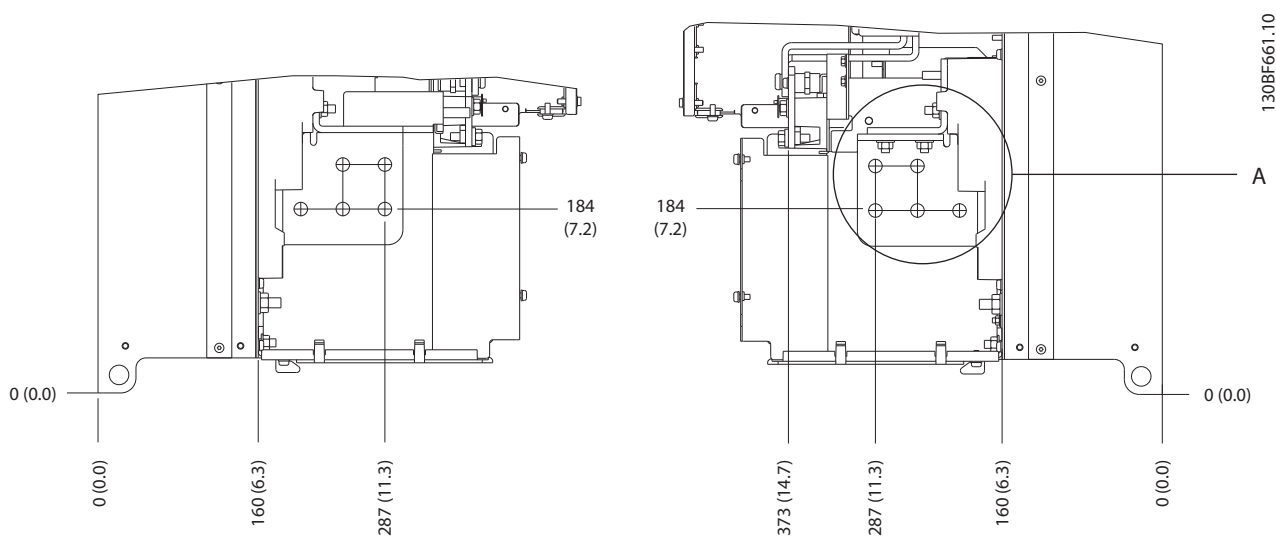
Terminaison du blindage RFI et dimensions de la plaque presse-étoupe du boîtier E3h
